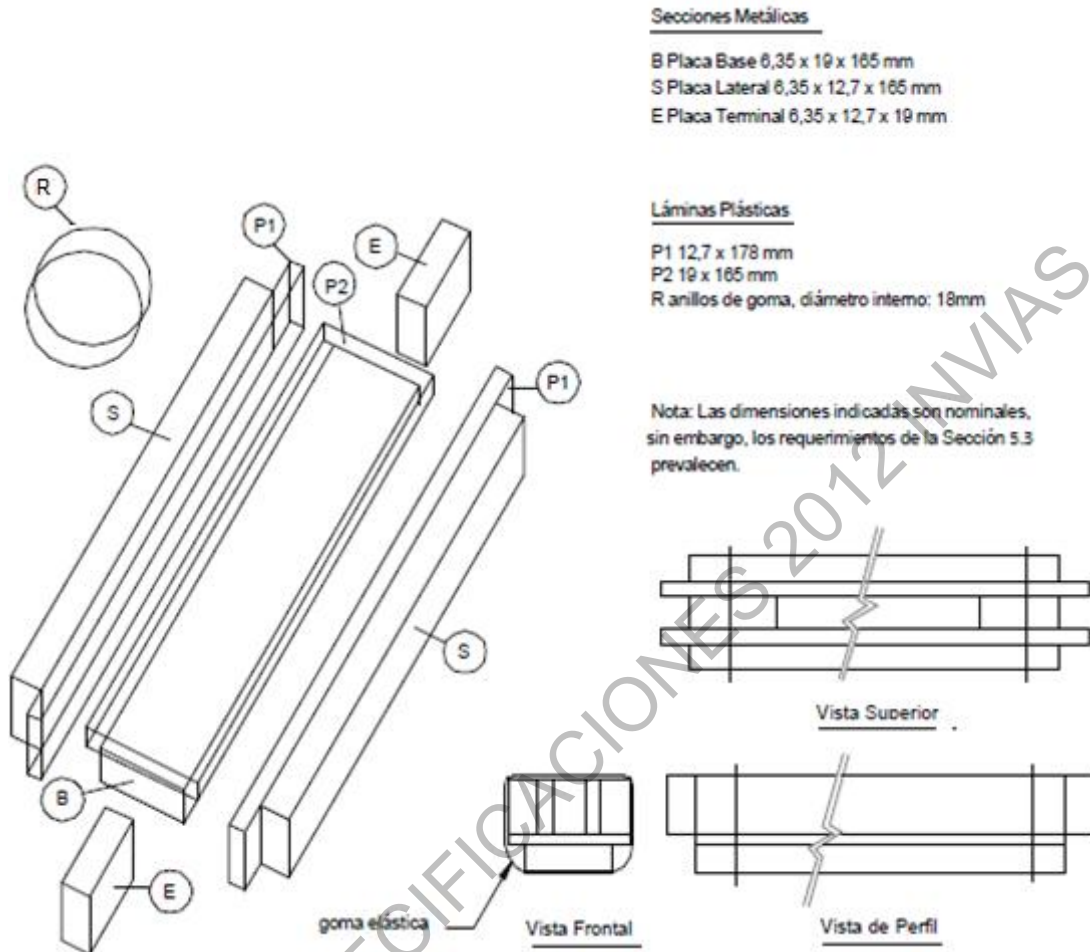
3. Dimensiones y especificaciones para los moldes de aluminio
